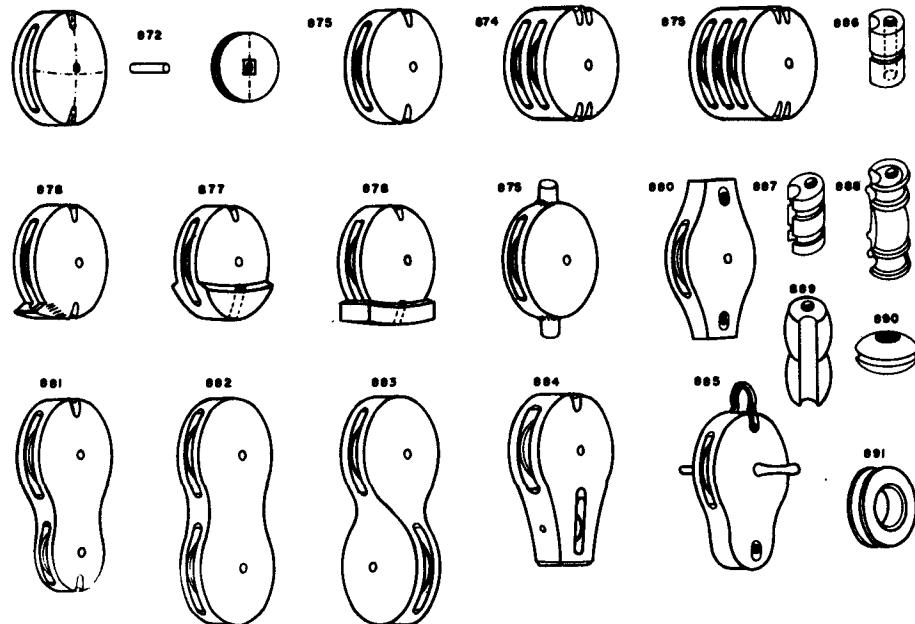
Части блока: корпус, ось или нагель и шкив
